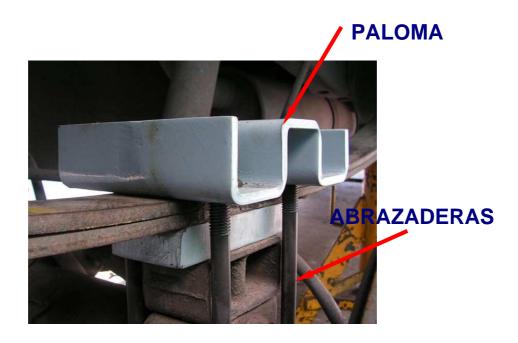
5. Colocación de la paloma. Vista tren trasero lado derecho.
